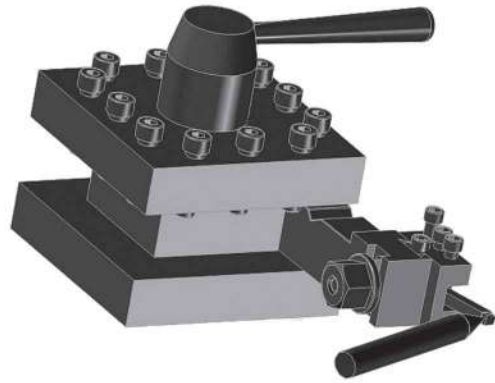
Isométrico para el montaje de torreta, portaherramienta y buril alineado con punto fijo
